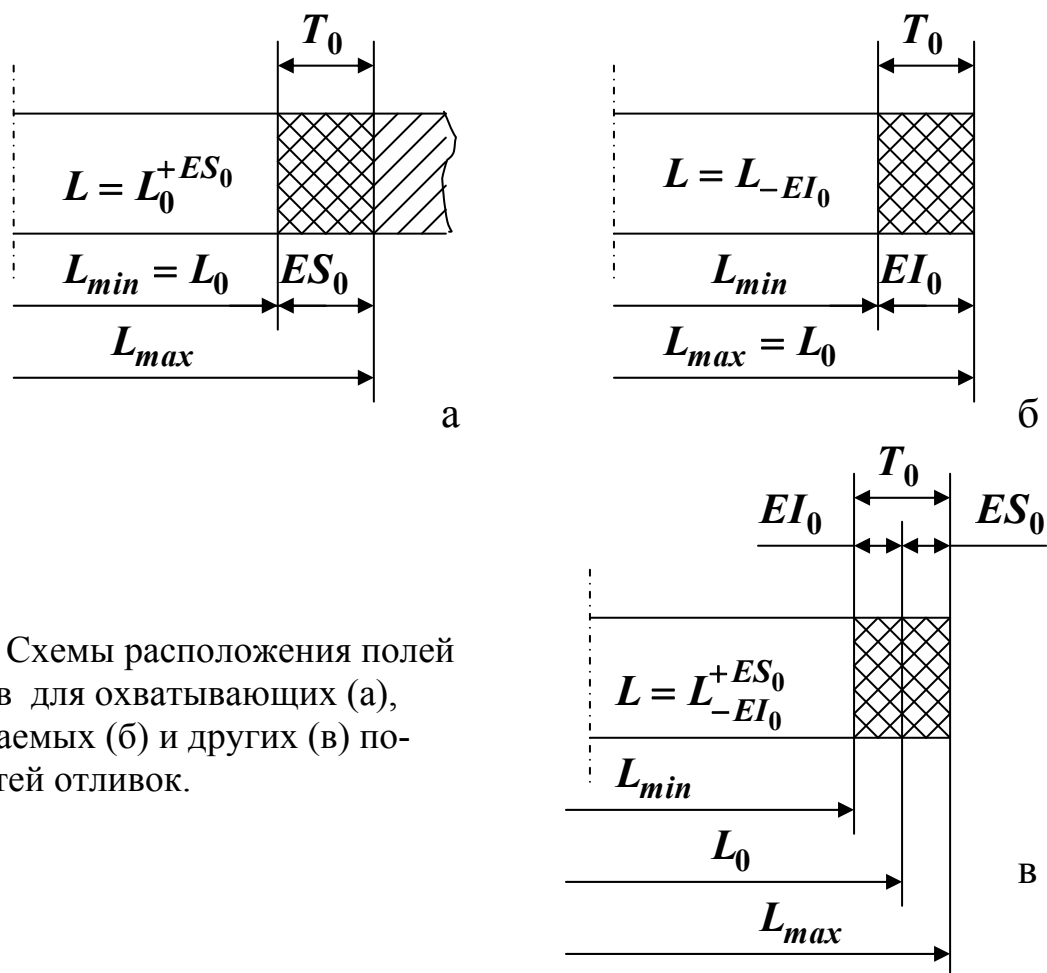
Схемы расположения полей допусков для охватывающих (а), охватываемых (б) и других (в) поверхностей отливок.
